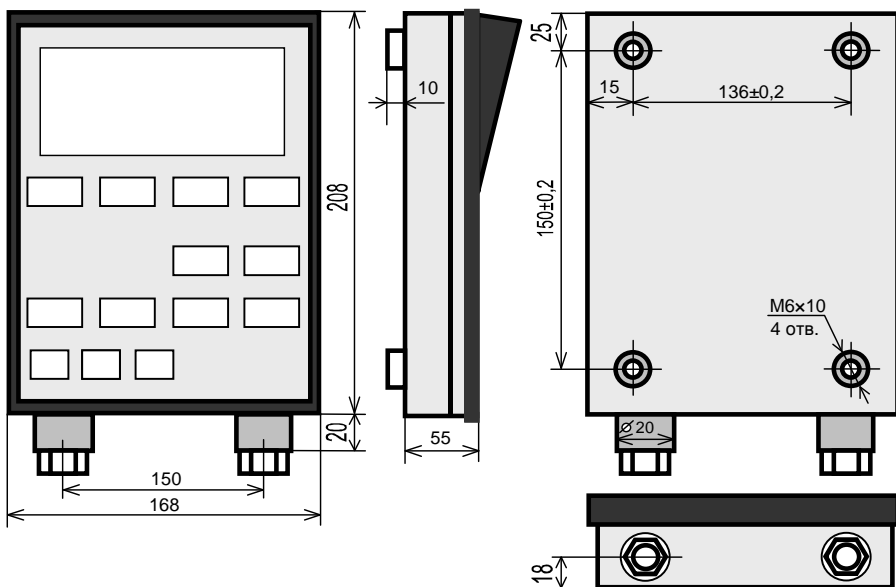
Габаритные и присоединительные размеры БОИ
